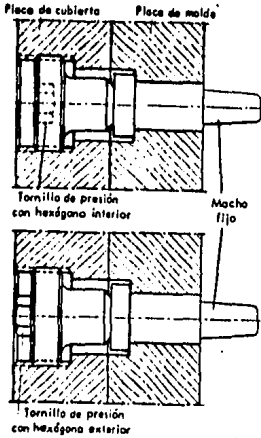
Sujeción de machos fijos mediante tornillos de presión.
